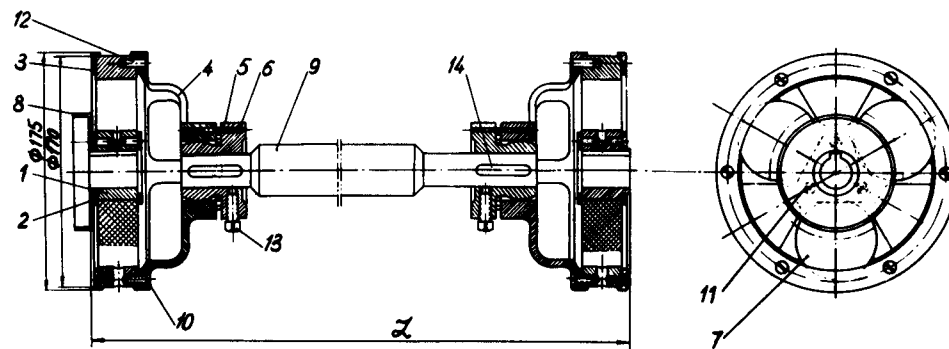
Муфты карданного вала. 1 - корпус муфты, 2 - шайба пружинная, 3 - кольцо пружинное, 4 - полумуфта, 5 - втулка шаровая, 6 - стержень, 7 - изолятор, 8 - втулка, 9 - вал, 10 - винт, 11 - штифт, 12 - винт установочный, 13 - шпонка.
